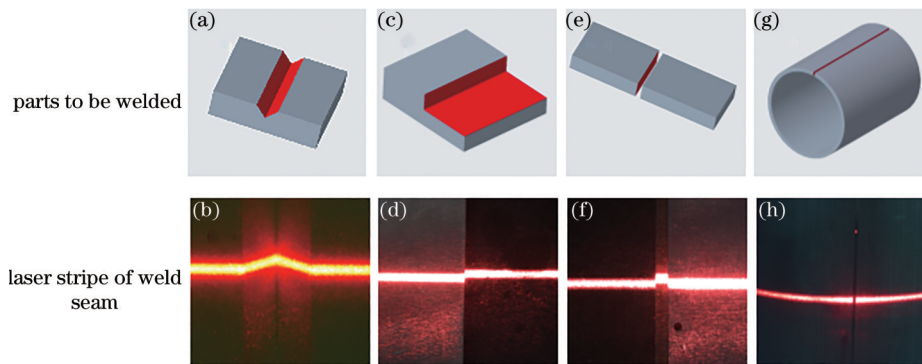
不同焊缝及对应激光条纹图。(a)(b) V型焊缝;(c)(d)搭接焊缝;(e)(f)拼接焊缝;(g)(h)管道焊缝
